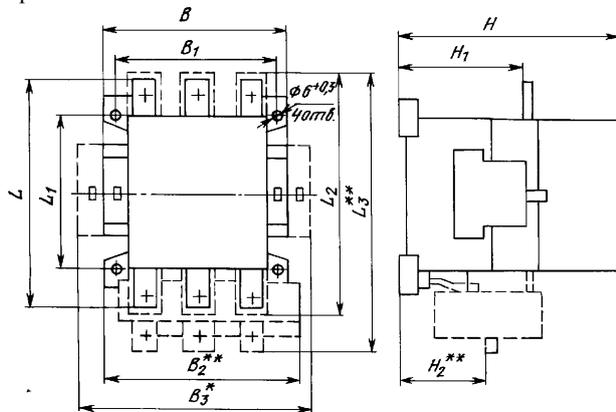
Габаритные, установочные размеры пускателей нереверсивных типов ПМ12-080, ПМ12-100 и ПМ12-160. Масса устанавливаемого на пускатель ограничителя перенапряжения не более 0,055 кг:
